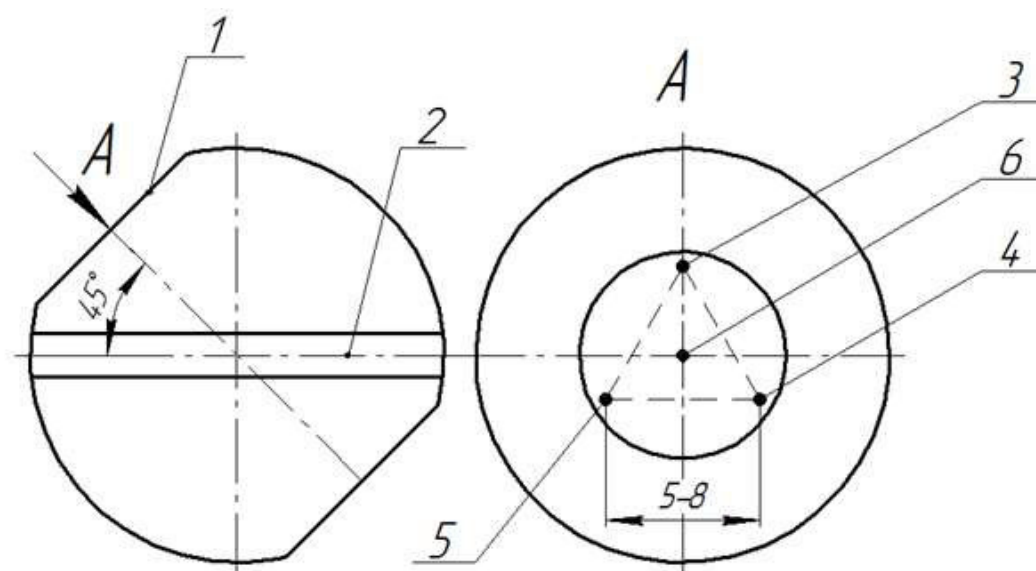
Схема изготовления площадок для контроля твердости поверхности шара:
